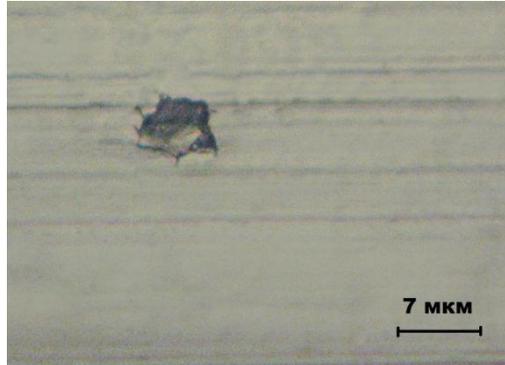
Раковина на поверхности дорожки качения кольца подшипника
